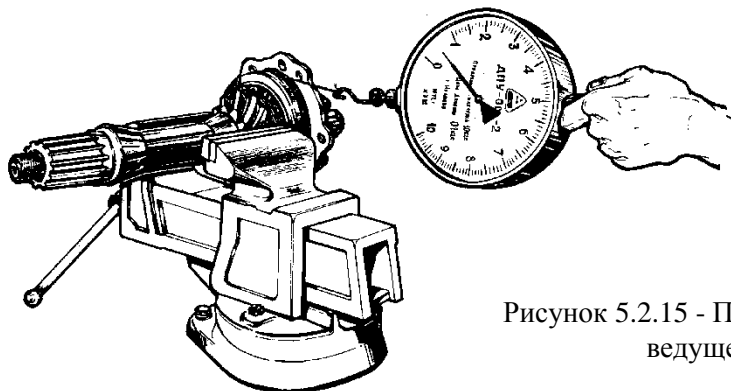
Проверка регулировки подшипников ведущей конической шестерни
